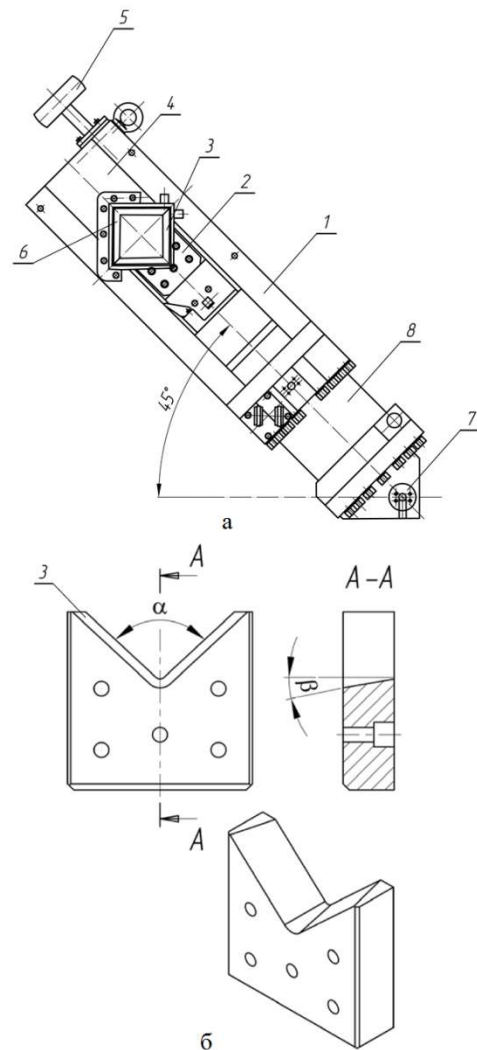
Загальний вигляд (а) ножиць летючих гідравлічних конструкції НКМЗ для поперечної гарячого різання на мірні довжини безперервно-литих квадратних заготовок і профілювання ножа (б): 1 – станина; 2, 4 – нижній і верхній супорт; 3, 6 – ножі; 5 – верхній ролик; 7 – циліндрична напрямна; 8 – гідроциліндр механізму різання
